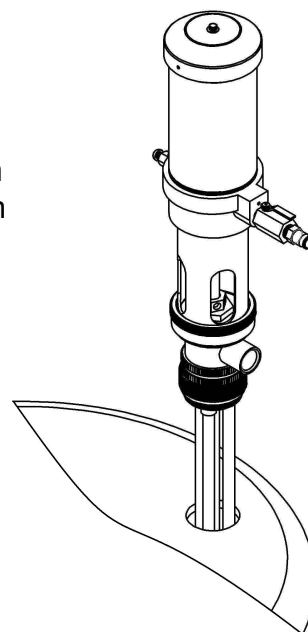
Figura B-instalação de equipamento de imagem com bomba e misturador de tambor. Set-up picture equipment installation with pump and drum mixer.
